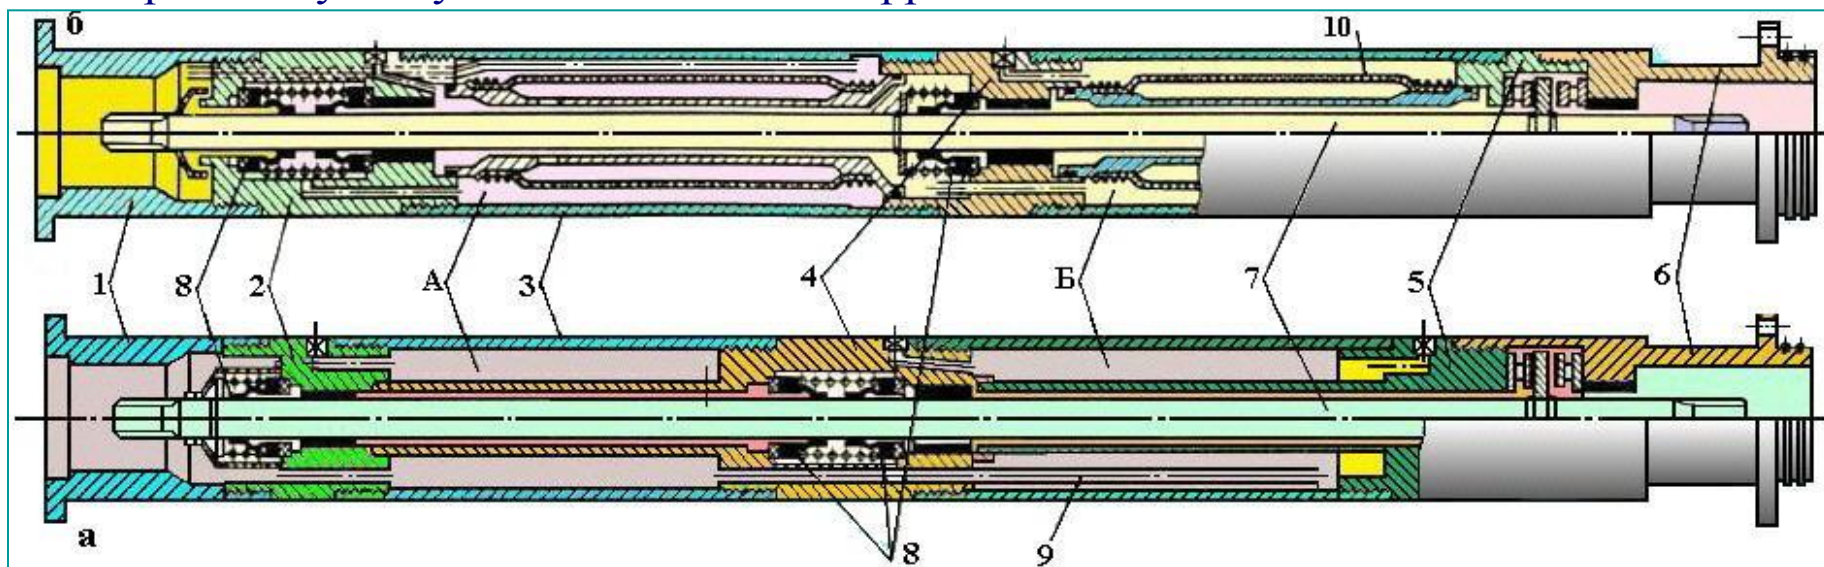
Гидрозащита открытого (а) и закрытого (б) типов: А - верхняя камера; Б - нижняя камера; 1- головка; 2- верхний ниппель; 3- корпус; 4- средний ниппель; 5- нижний ниппель; 6- основание; 7- вал; 8- торцовое уплотнение; 9- соединительная трубка; 10 - диафрагма.
